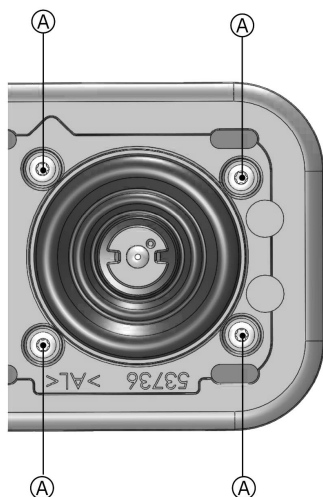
Sätt tillbaka och dra åt skruvarna A.
